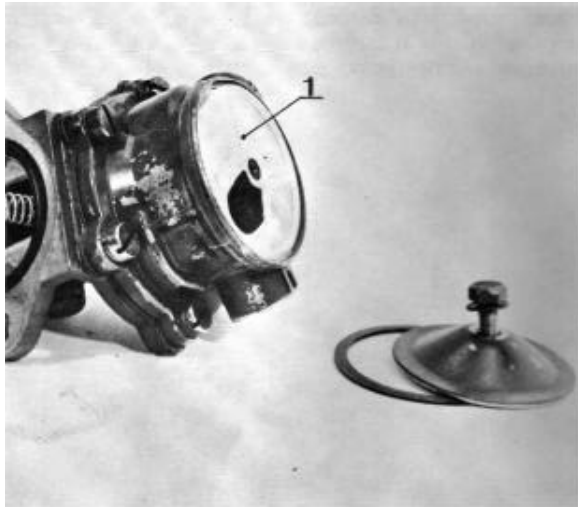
, sil i matarpumpen som ska rensas i samband med filterbyte, man skymtar den svarta o-ring som tätar mot motorblocket längst till vänster i bilden.
